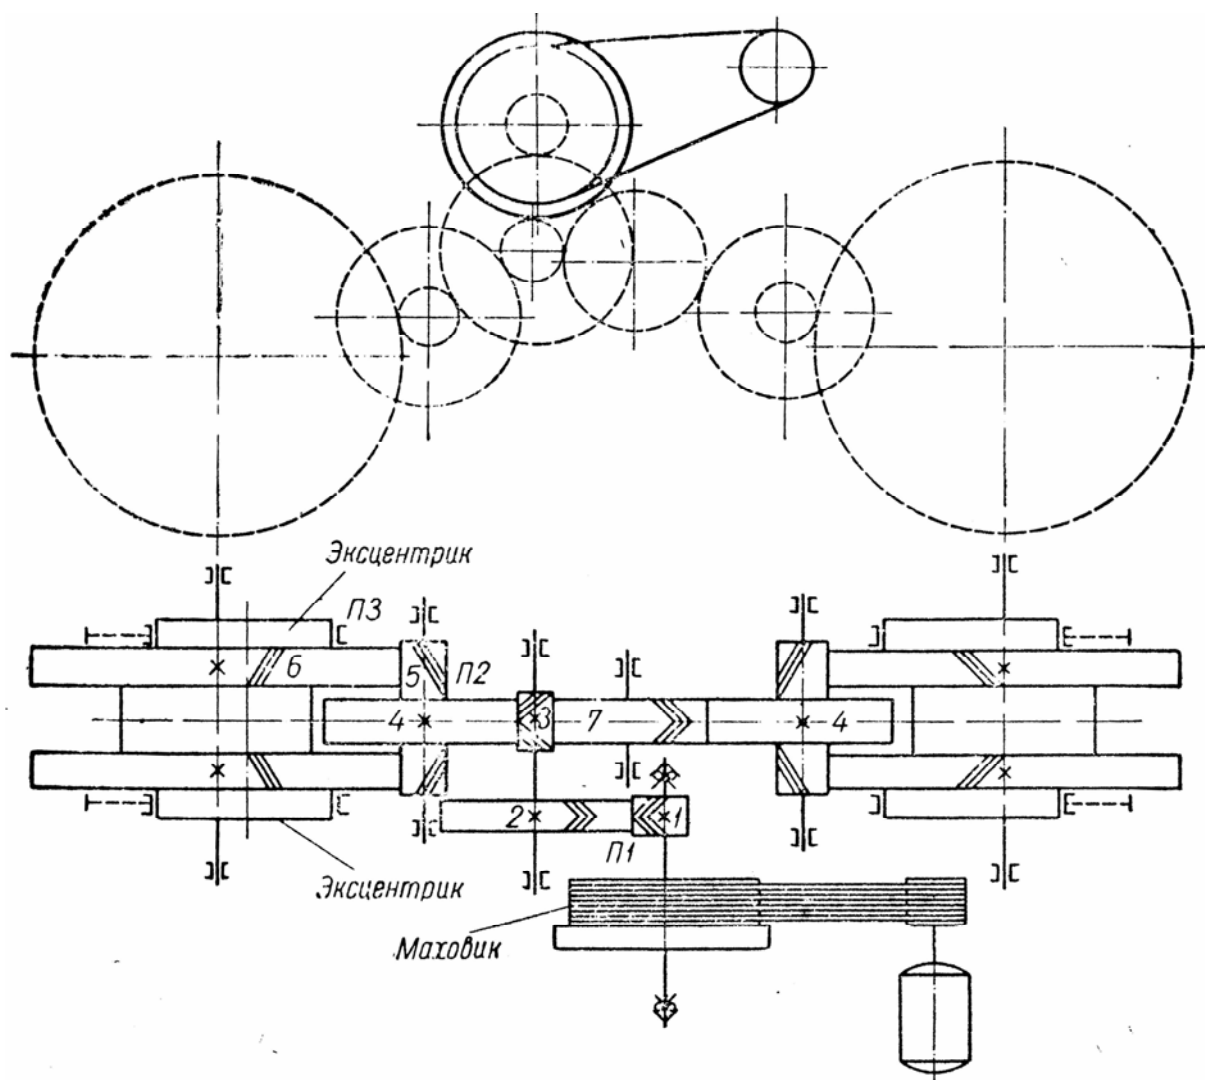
Кінематична схема передач механічного ексцентрикового преса
